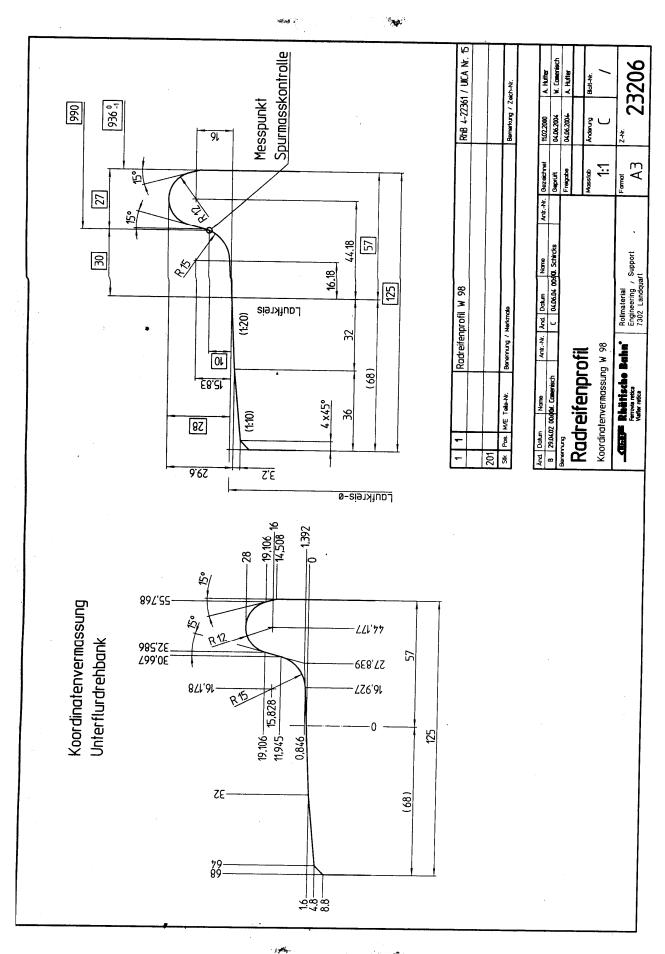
Рабочий чертеж колеса Ø 750 мм ( ссылочный черт. № 29240, ред. Е )
